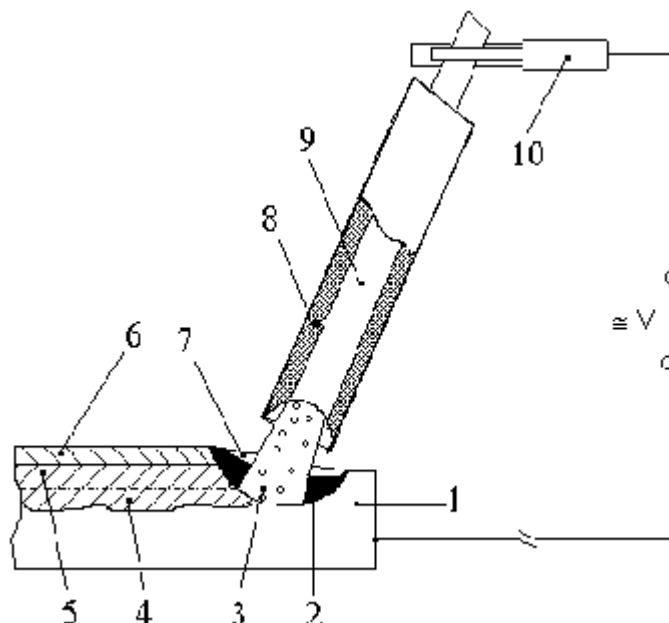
Схема ручной дуговой сварки штучным электродом: 1 – основной металл; 2 – сварочная ванна; 3 – электрическая дуга; 4 – проплавленный металл; 5 – наплавленный металл; 6 – шлаковая корка; 7 – жидкий шлак; 8 – электродное покрытие; 9 – металлический стержень электрода; 10 – электрододержатель
